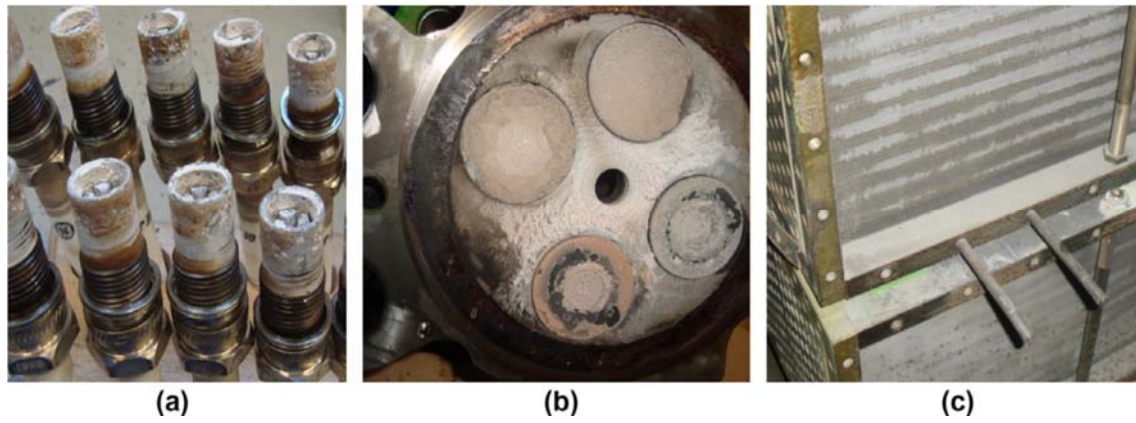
Abrasión producida en diferentes partes del motor de combustión: (a) bujías, (b) cabezal del motor, (c) intercambiador del radiador [13].
